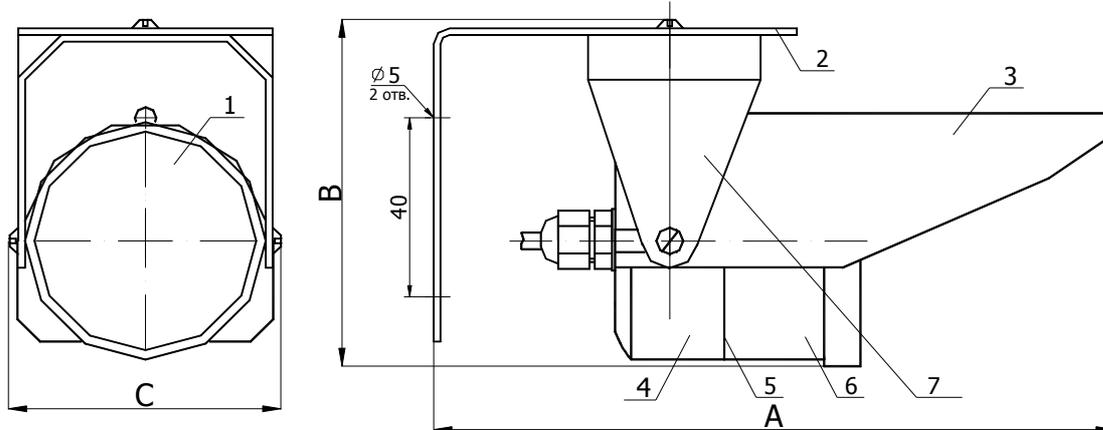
Общий вид извещателя ИД-40, ИД-50
